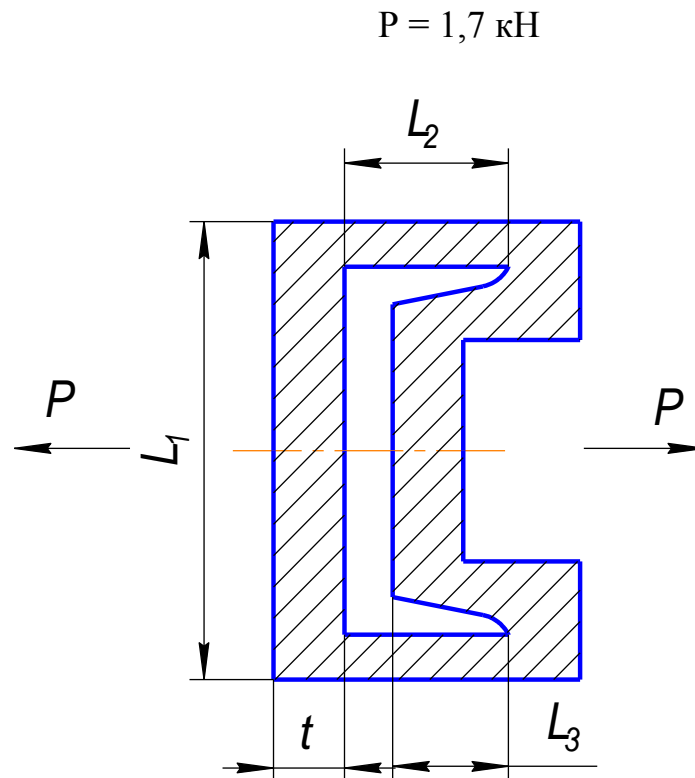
Розрахункова схема зварювального кріплення кронштейна до рами
